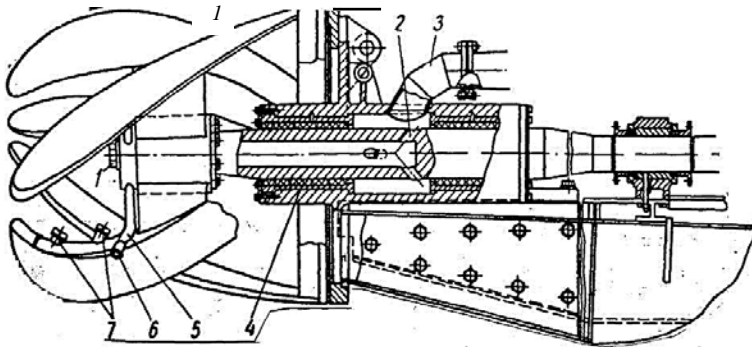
Фрезерно-гидравлический разрыхлитель: 1 – лобовая насадка; 2 – каналы; 3 – водопровод; 4 – головной подшипник; 5 – подающие патрубки; 6 – боковые разрыхляющие насадки; 7 – смазывающе-подводящие насадки
